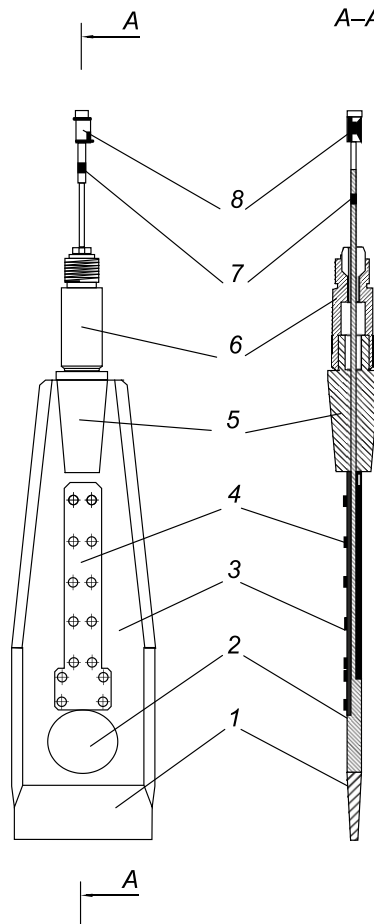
Конструкция дилатометра: 1 – наконечник; 2 – датчик давления; 3 – пластина; 4 – крышка канала вывода кабеля; 5 – конус; 6 – переходник с резьбой под штангу; 7 – кабель; 8 – разъем
